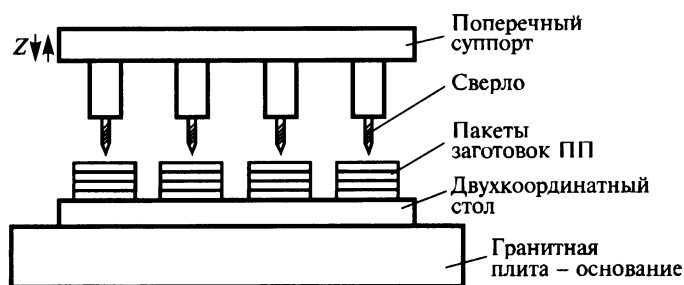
Схема четырехшпиндельного сверлильного станка
